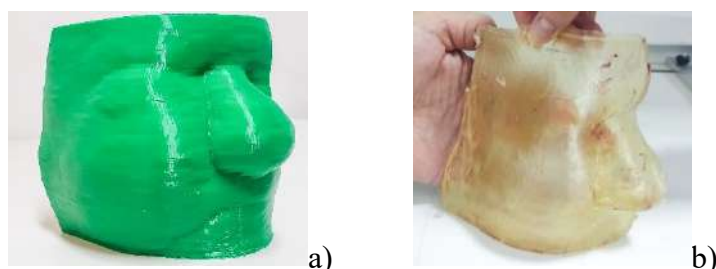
a): Molde personalizado impresso em PLA e b) resultado do bolus de gelatina após desenforme do molde
